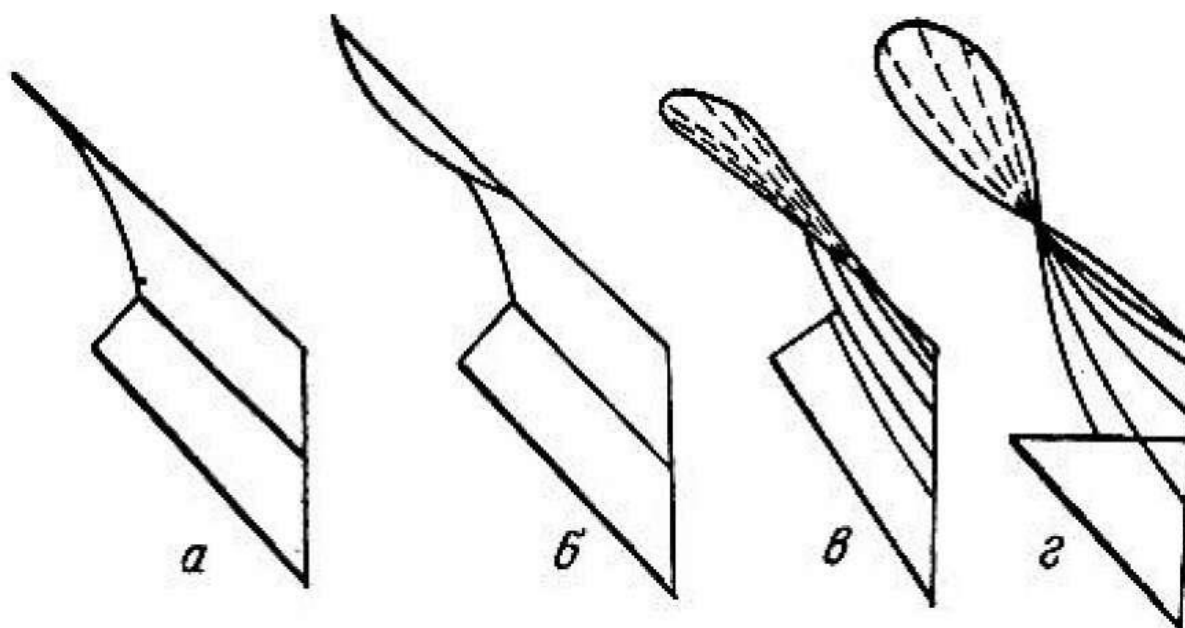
Типи відвальних поверхонь плужного корпусу: а - циліндрична; б - культурна; в - напівгвинтова; г - гвинтова
